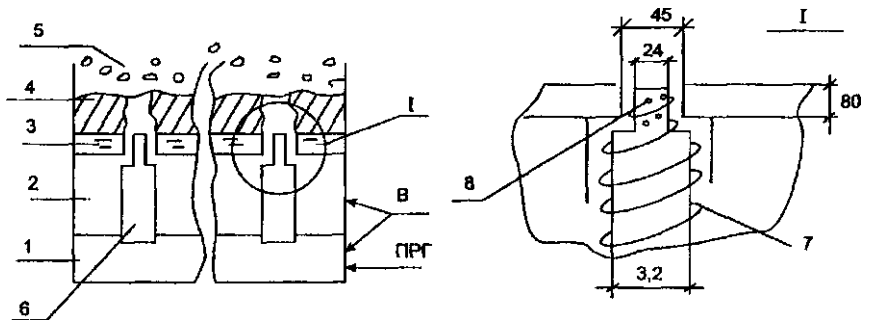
Принципиальная схема горелки прямого сжигания природного газа: 1 - камера смешения первичного воздуха с природным газом; 2 - камера подвода вторичного воздуха; 3 - водоохлаждаемая продувочная решетка; 4 - твердый слой гарниссажа; 5 - слой расплава; 6 - трубка подвода газозвушной смеси; 7 - завихритель воздуха; 8 - отверстия выхода газозвушной смеси; В - воздух, ПРГ - природный газ
